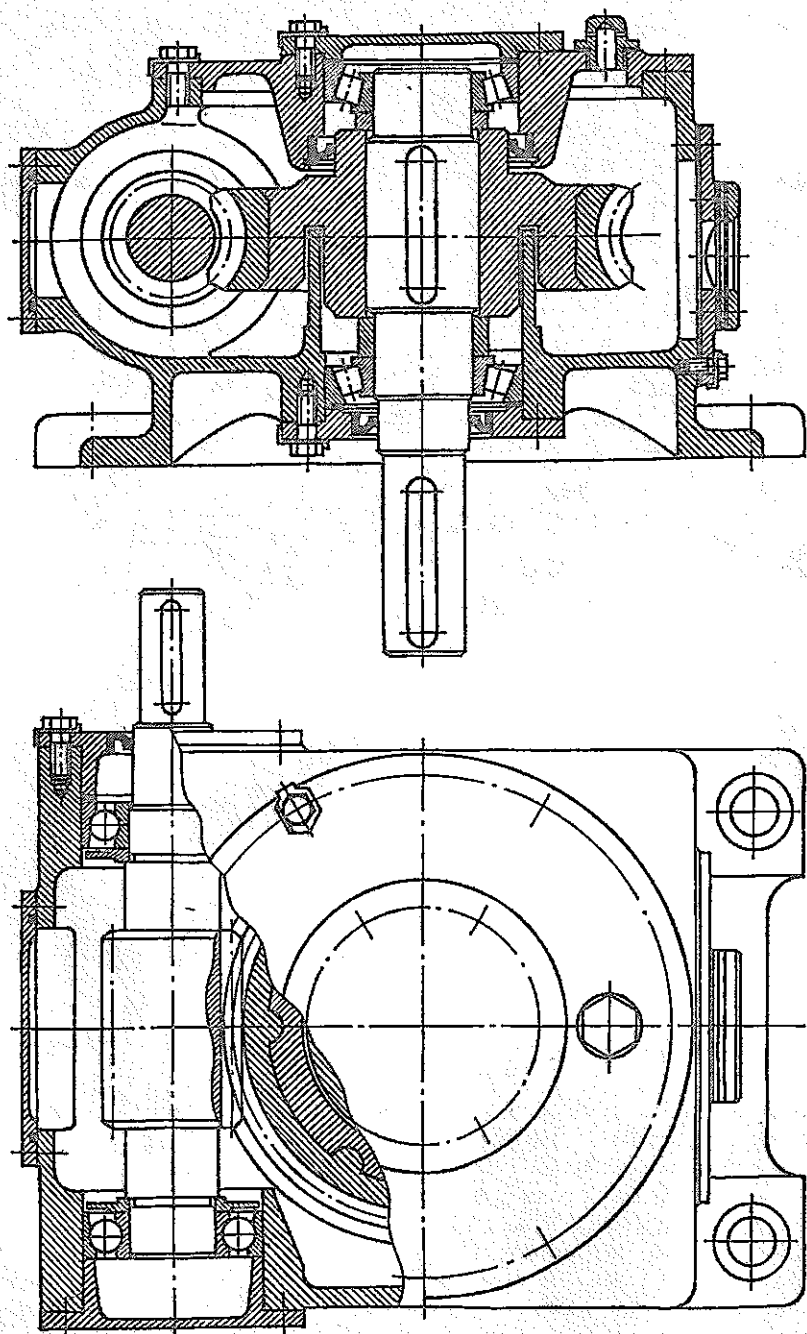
Одноступенчатый червячный редуктор с вертикальным валом червячного колеса
